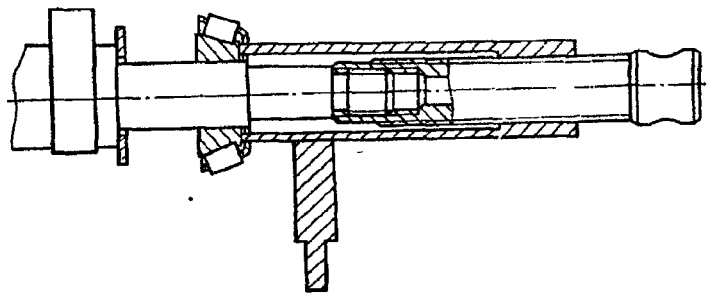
Приспособление И801.27.000 для установки подшипников кулачкового вала ТНВД
